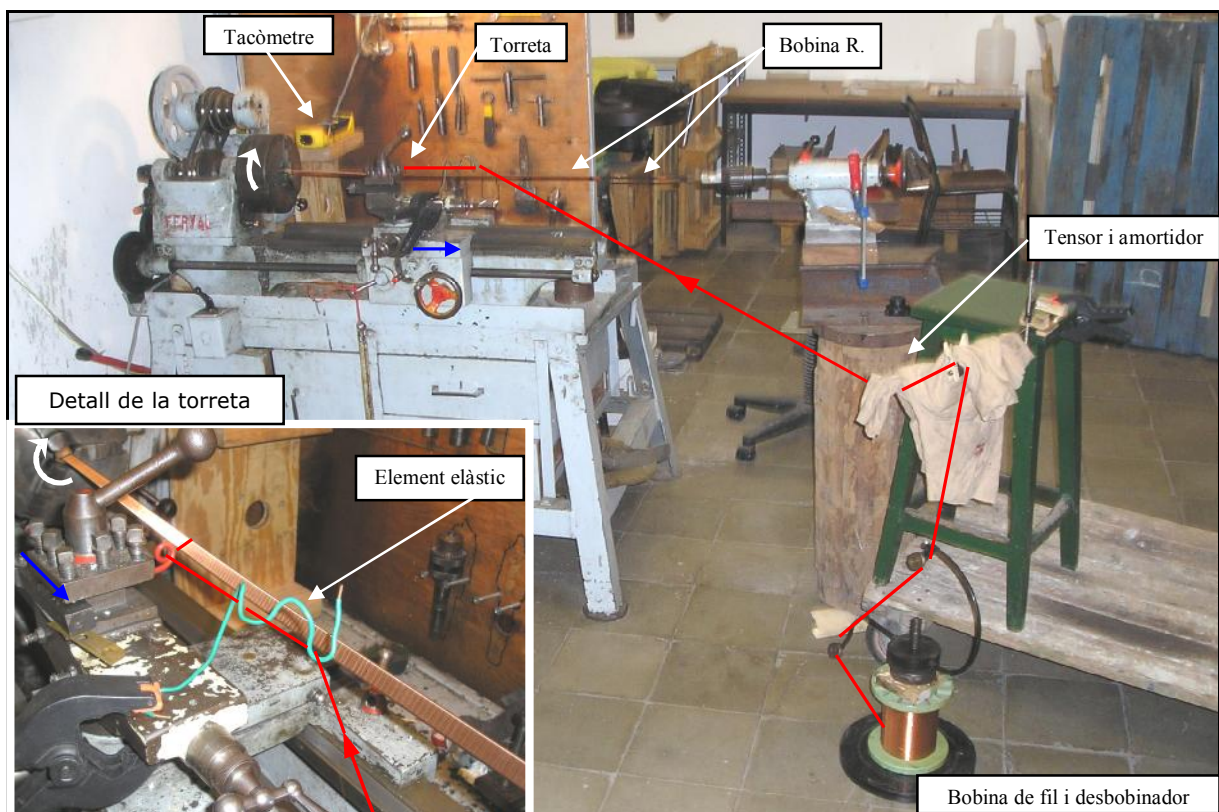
Disposició dels elements per bobinar: torn i elements auxiliars.
